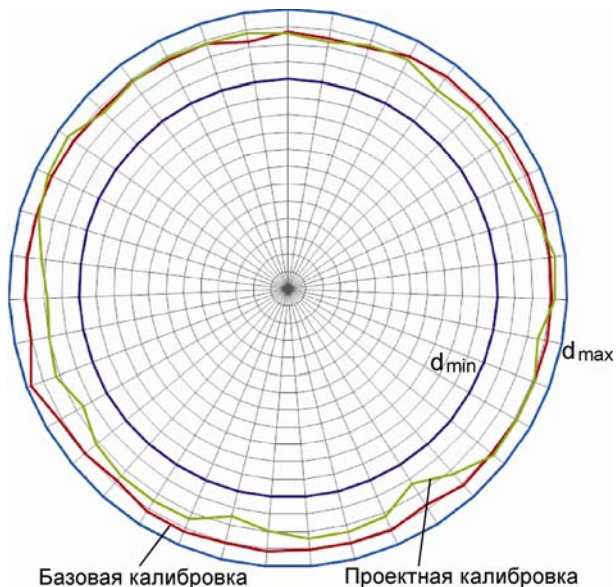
Схема поперечного сечения катанки с построением фактической геометрии профиля, полученного по двум различным в построении калибровкам с указанием предельных допусков на геометрические размеры
